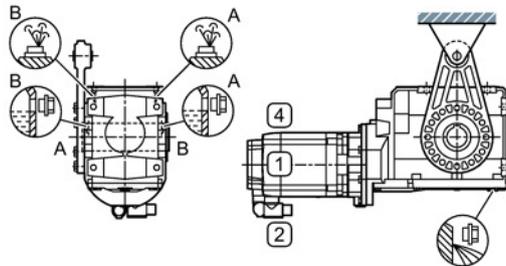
Einbaulagen für Kegelaradgetriebe BAD, Aufsteckausführung, Baugröße 29, 2-stufig
